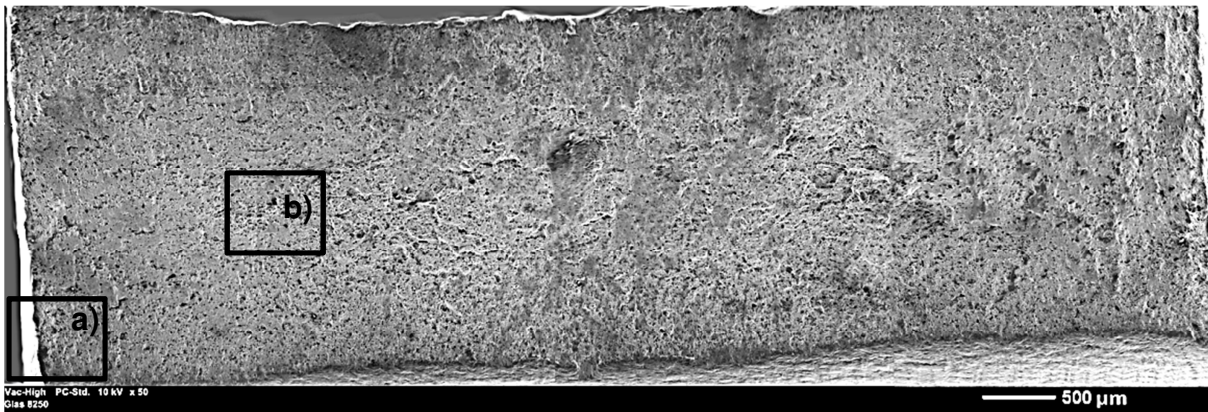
exemplarische REM Bruchflächenaufnahme einer EN AW-5454-O Zugprobe
